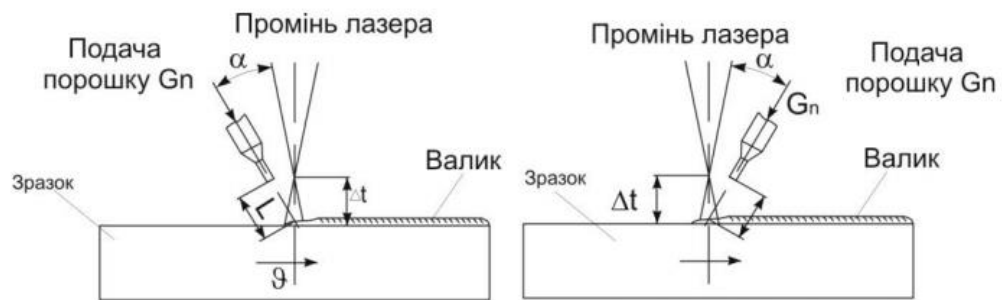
Схема газопорошкового лазерного наплавлення з подачею порошку вслід руху (а) і назустріч руху (б) зразка.
